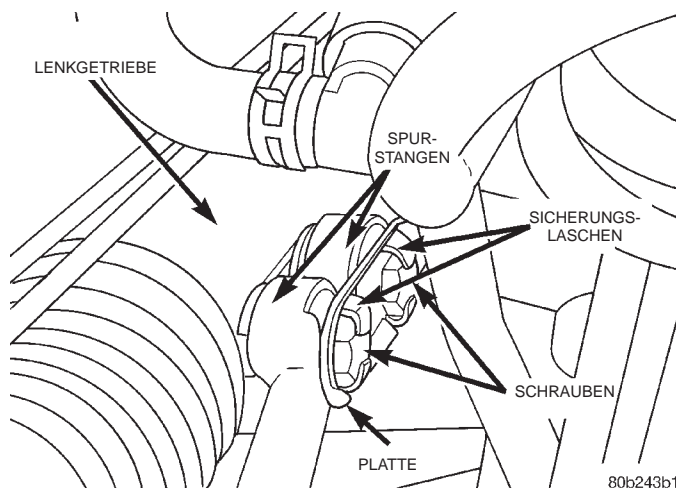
Sicherungslaschen/Befestigungsschrauben der Spurstange
